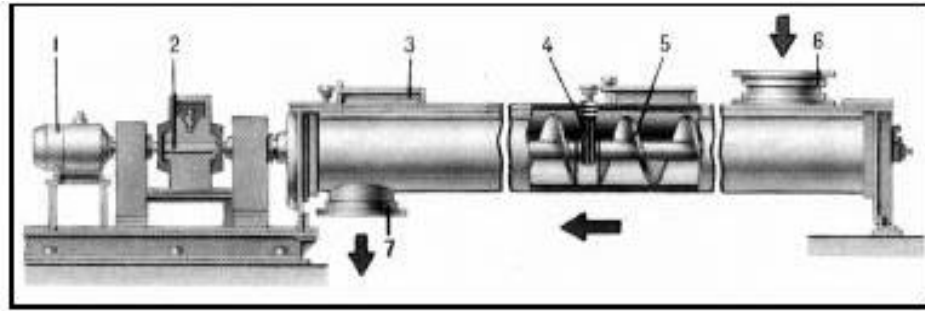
Конструктивна схема шнекового транспортера у загальному вигляді: 1 – механізм приводу; 2 – редуктор; 3, 6 – завантажувальні бункері; 4 – кожух; 5 – гвинтовий конвеєр; 7 – вивантажувальний шибер
